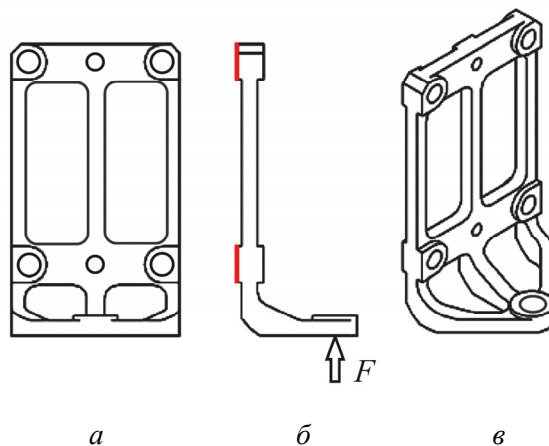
Исходный вид кронштейна (красным цветом указаны поверхности закрепления, F – нагрузка): a – вид спереди; b – вид сбоку; c – вид под углом 45°
